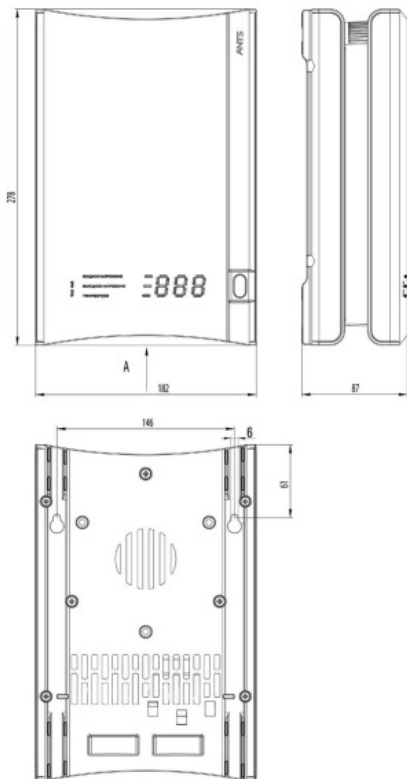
Габаритные и установочные размеры стабилизаторов КилоГерц У 1-8
